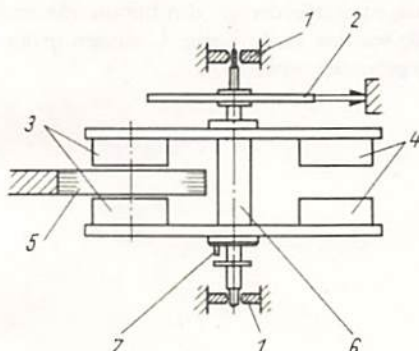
Drehschwinger mit schwingendem Dauermagnetsystem
